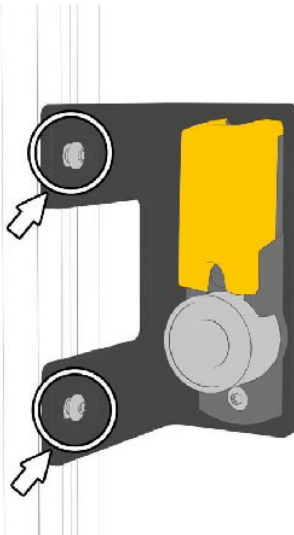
Montageplatte mit Prozesszuhaltung am Profil anbringen und und Schrauben M8 x 12 mm Torx festziehen.
